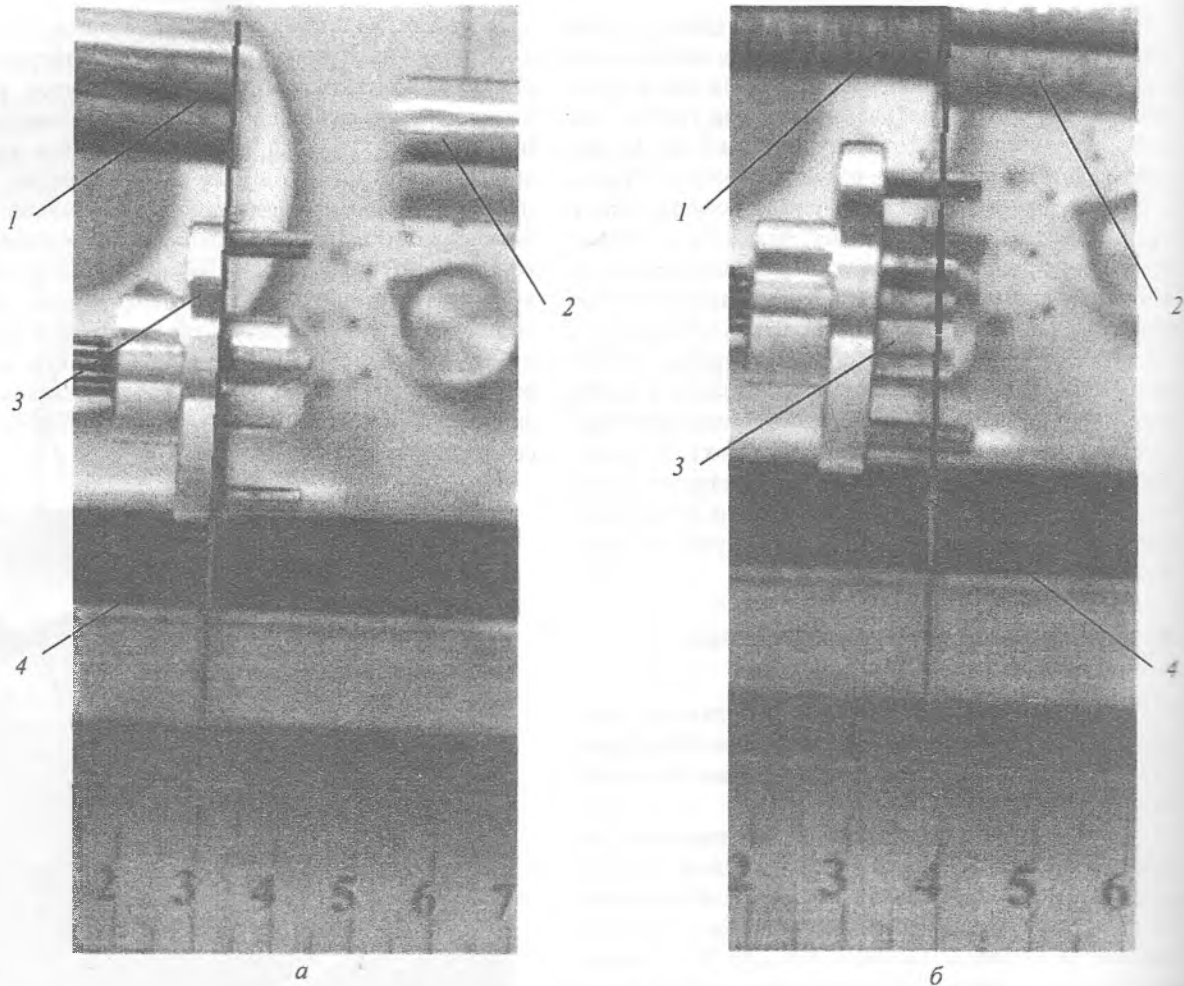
Положение заготовки распиловочного диска, свободно установленной на оправке, до контактирования с деформирующими инструментами (а) и после (б)
